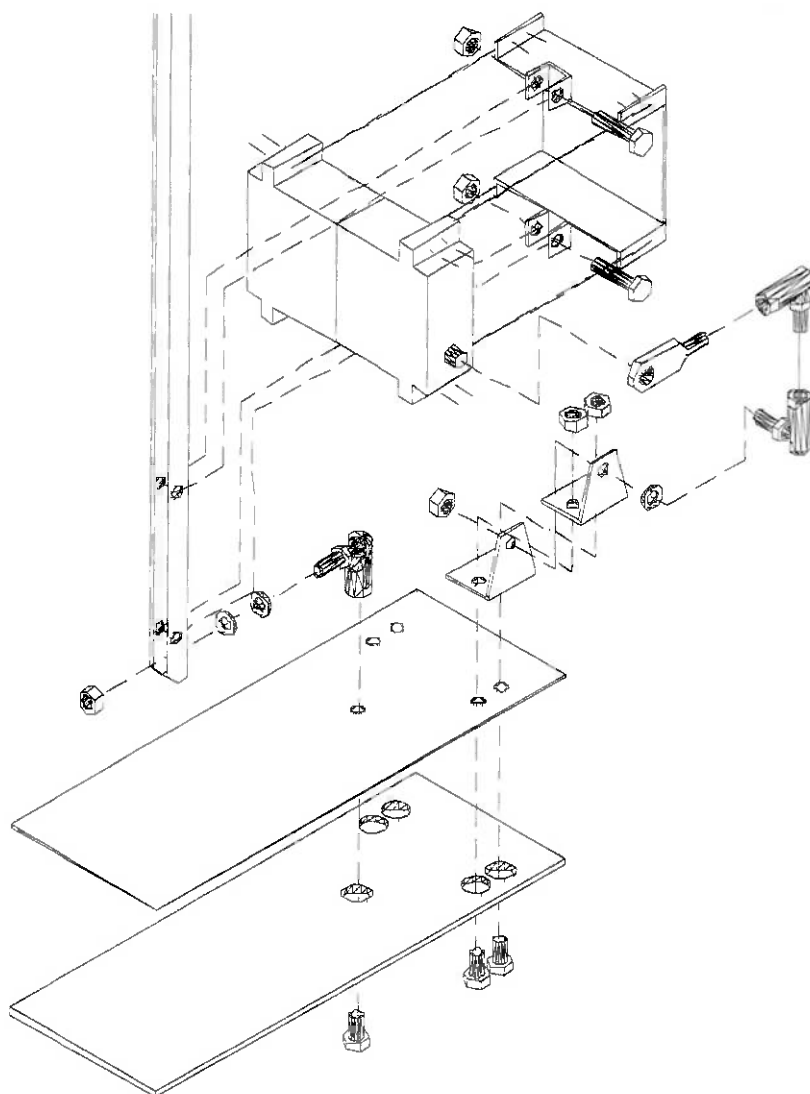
Desenho de conjunto do quadril - vista traseira
